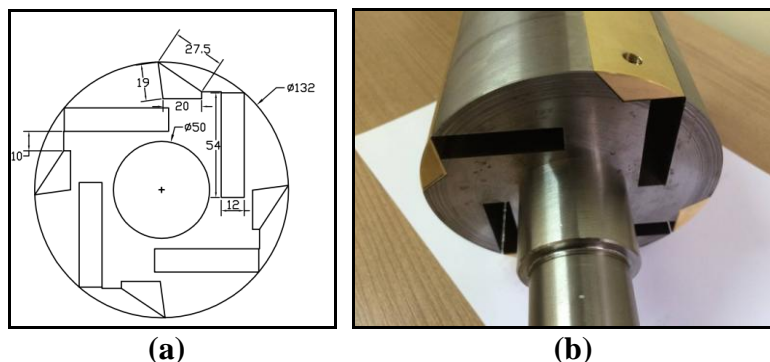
Rotor com ímãs embutidos – (a) Desenho esquemático – (b) rotor montado [12]
